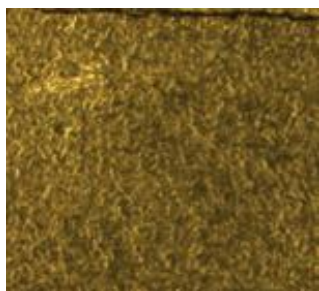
Общий вид пластины с покрытием порошка для наплавки ПГ – СР4 – ОМ, x 5
